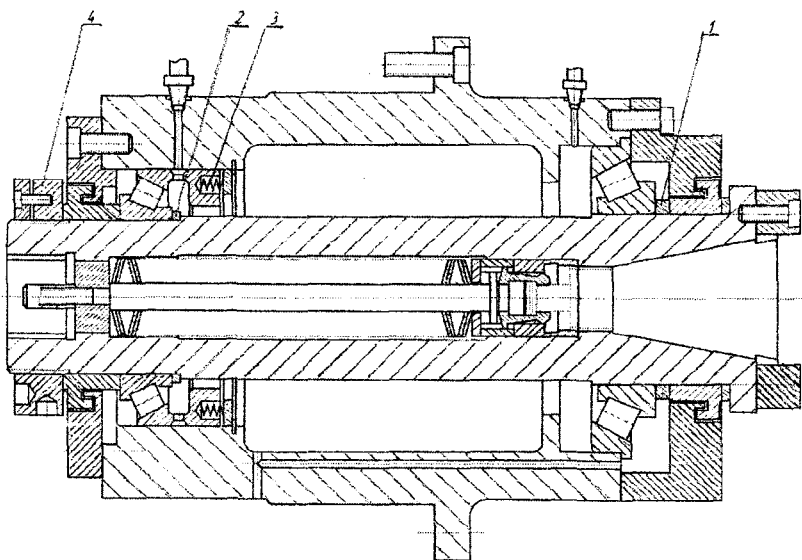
Шпиндельный узел с роликовыми радиально-упорными однорядными коническими подшипниками с упорным бортом на наружном кольце типа 67000 в передней опоре и с мягкой выборкой зазоров типа 17000 в задней
